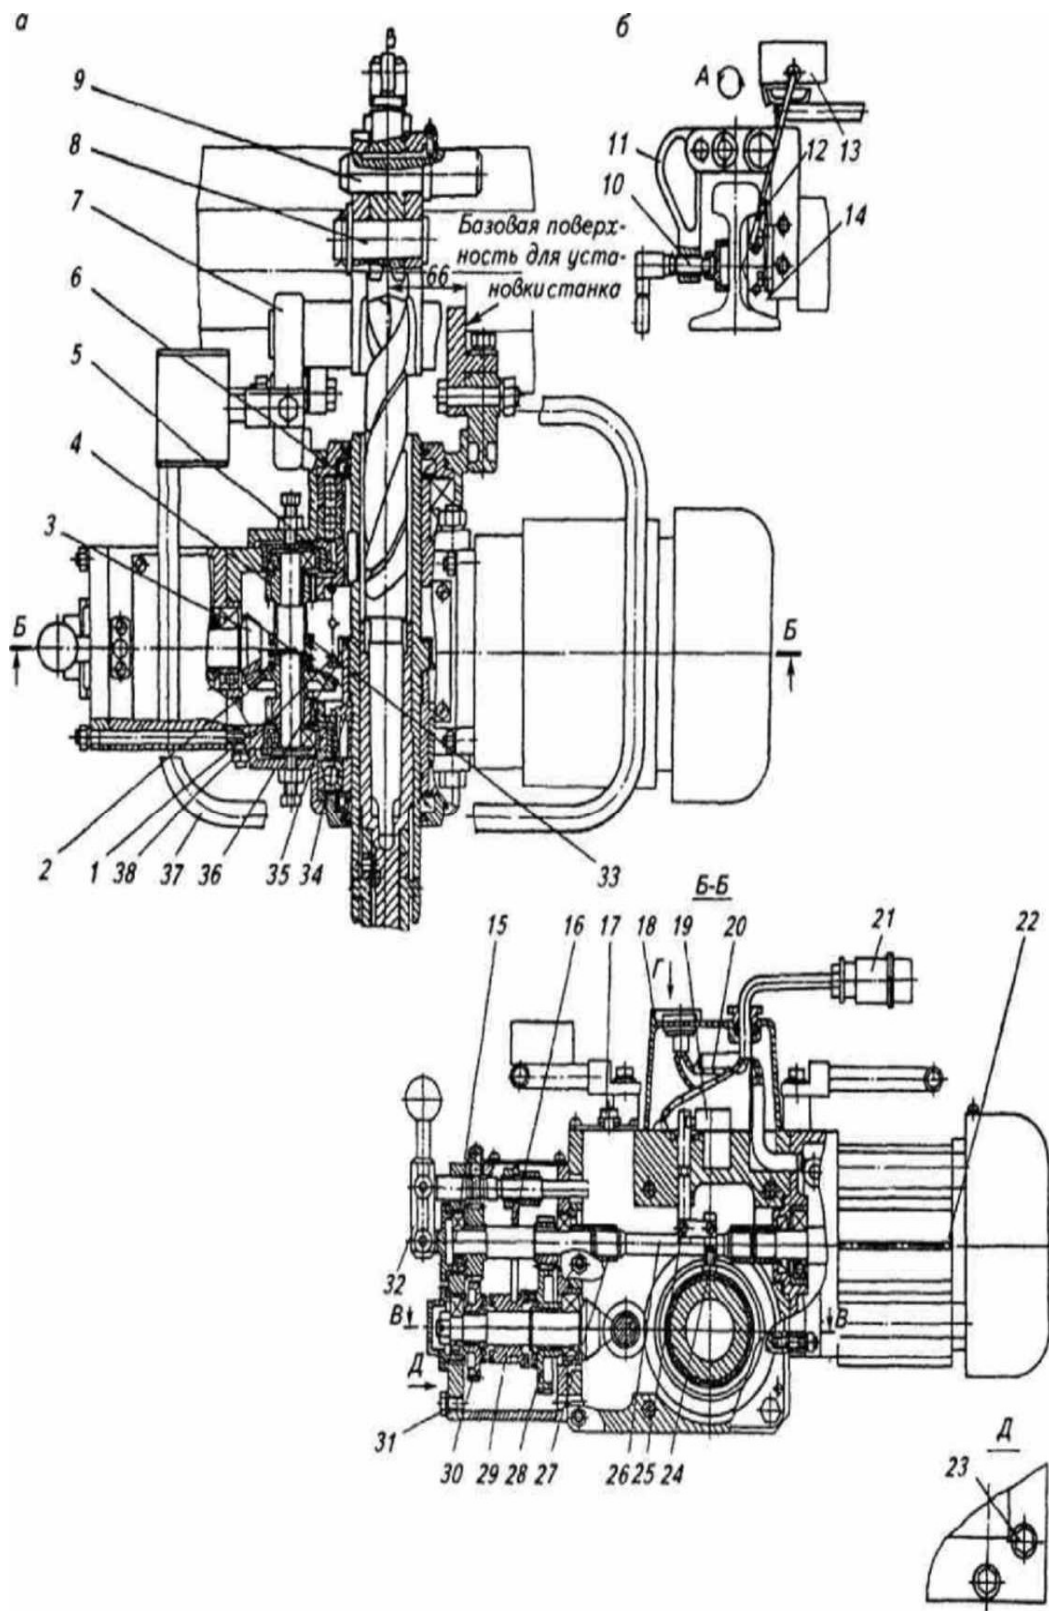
Конструкция станка рельсосверлильного СТР 2 а- вид сверху, б- узел зажима, в- разрез.
